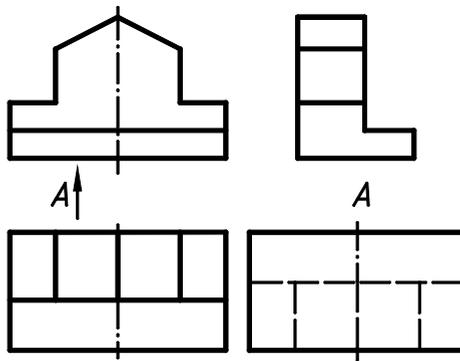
Amplasarea proiecțiilor în plan
